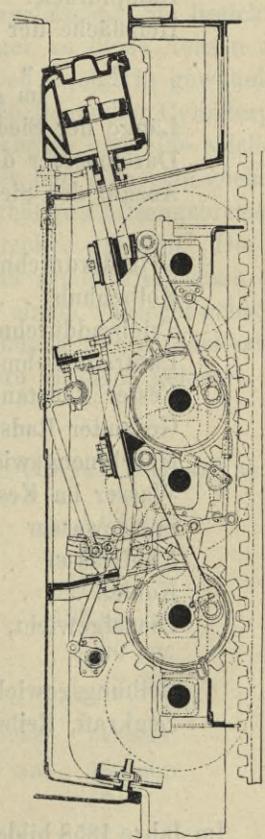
Zahnradanordnung der Bosnisch-herzegowinischen Lokomotiven.
